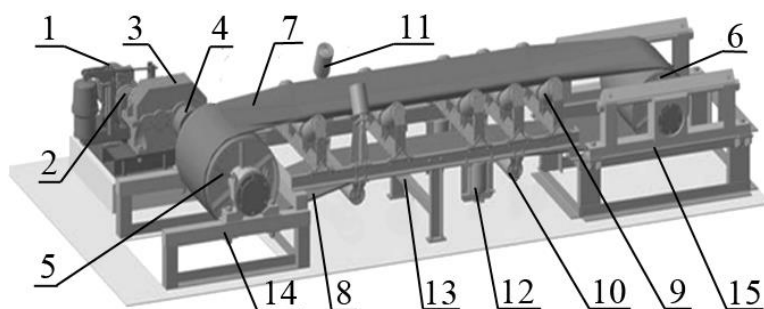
Конструкція та основні вузли стрічкового конвеєра
